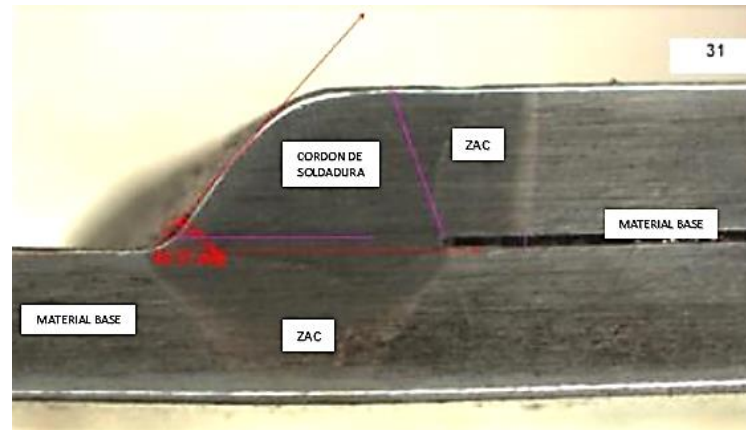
Macrografía y visualización de zonas generadas por soldadura
